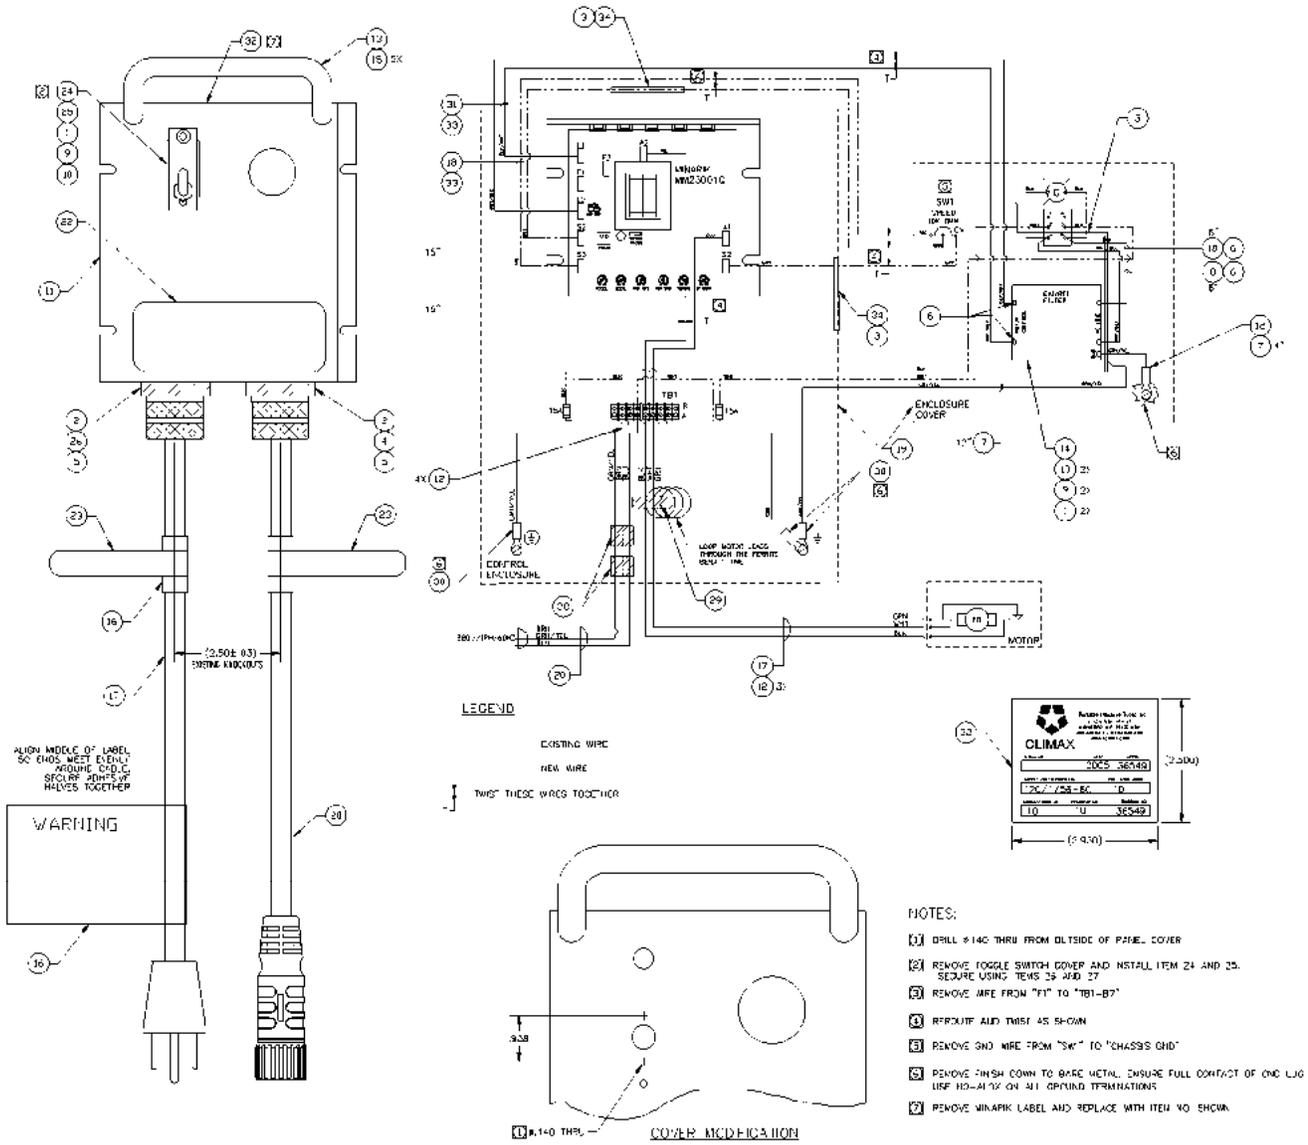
СХЕМА ШПИДЕЛЯ 120 В WELDON 36549
